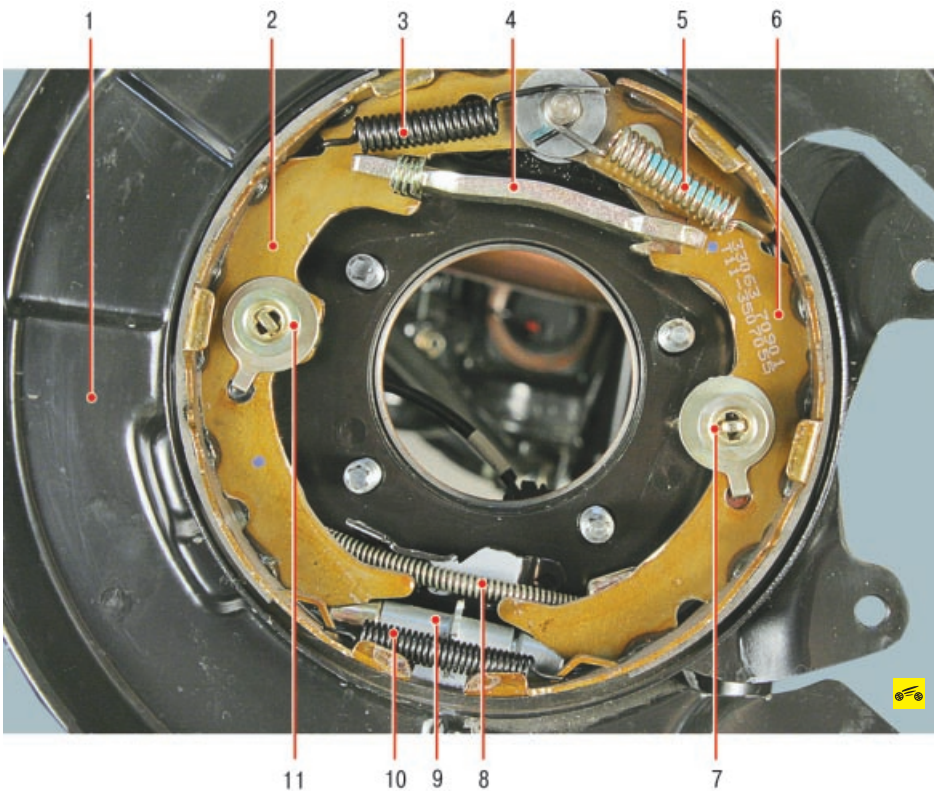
Стояночный тормозной механизм заднего колеса: 1 – опорный щит стояночного тормоза; 2 – передняя колодка стояночного тормоза; 3 – стяжная пружина передней колодки; 4 – распорная планка; 5 – стяжная пружина задней колодки; 6 – задняя колодка стояночного тормоза; 7, 11 – опорные стойки колодок; 8 – трос привода стояночного тормоза; 9 – регулировочное устройство; 10 – нижняя стяжная пружина колодок
